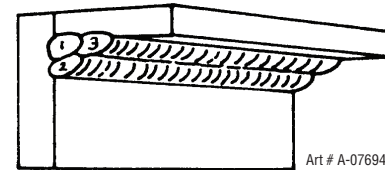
Posición elevada, soldadura de ángulo
